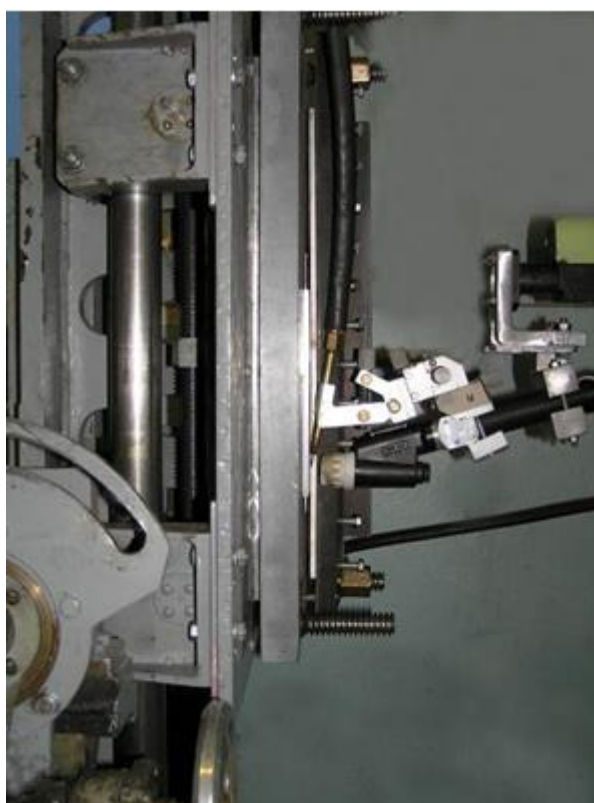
Установка, налаштована для виконання вертикального зварювального шва на вертикальній поверхні
